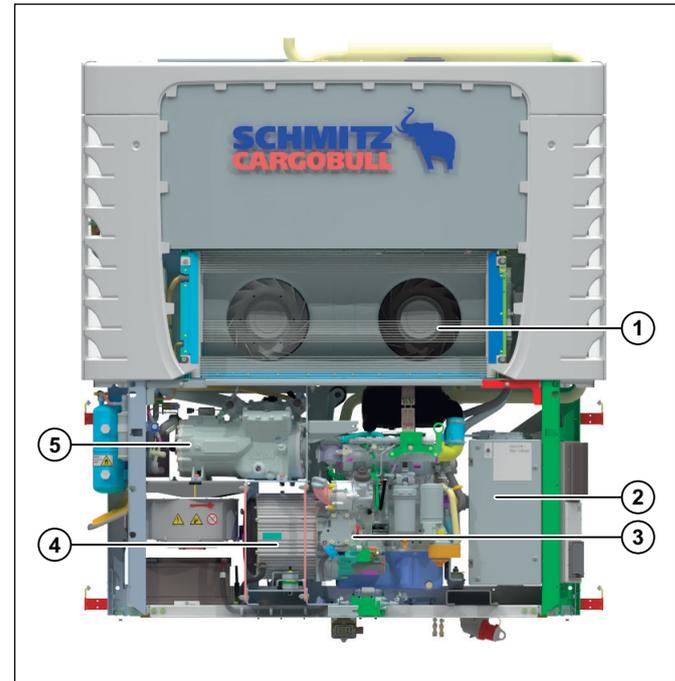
Вид с открытыми дверцами (S.C.U dc90)
